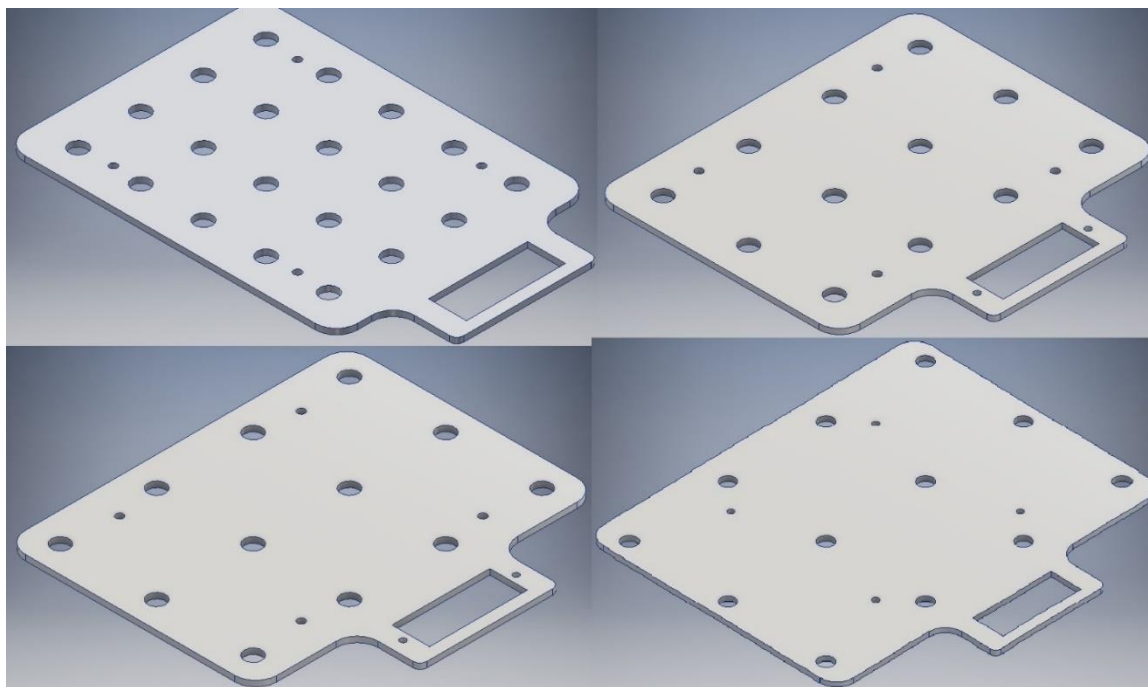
PLACA SUPERIOR DEL MECANISMO DE SUJECIÓN.
